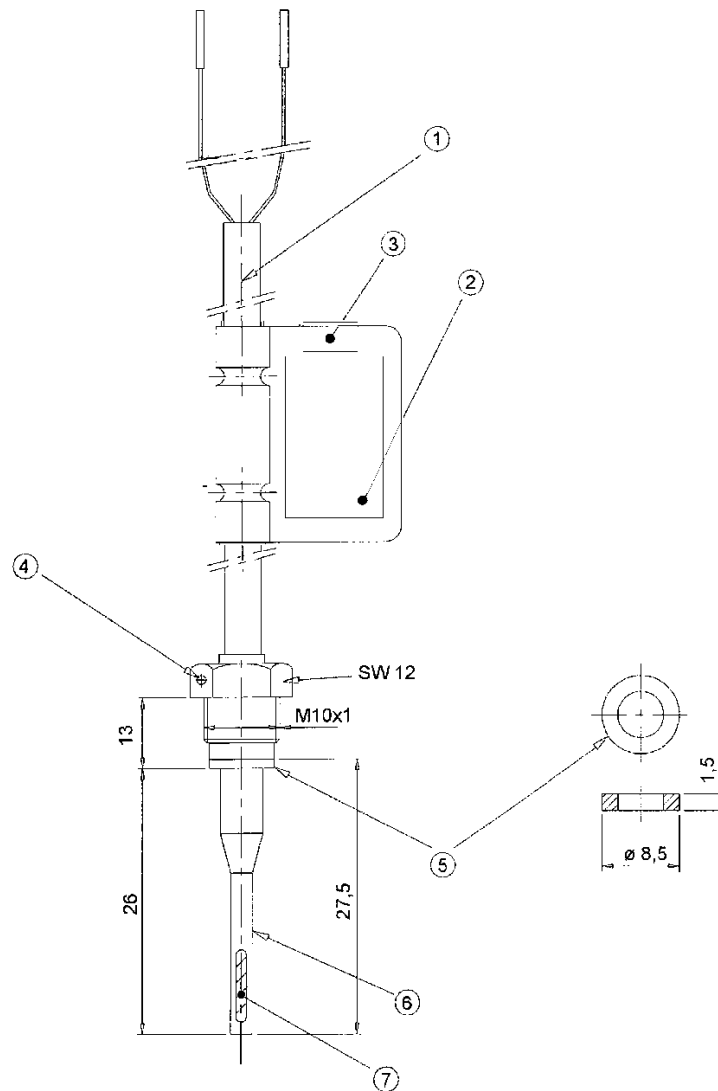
Габаритные, установочные и присоединительные размеры термопреобразователя типа DS.
